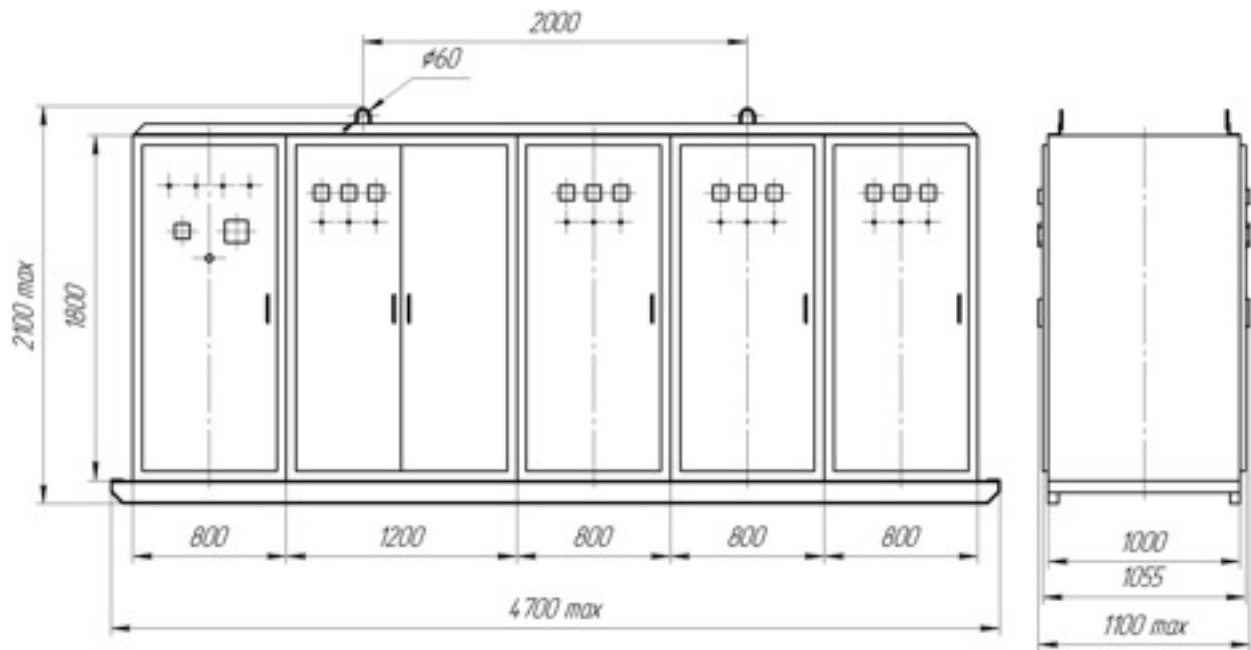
Габаритные размеры и масса установки УКВ РН-6,3-3600-450-УХЛ5
